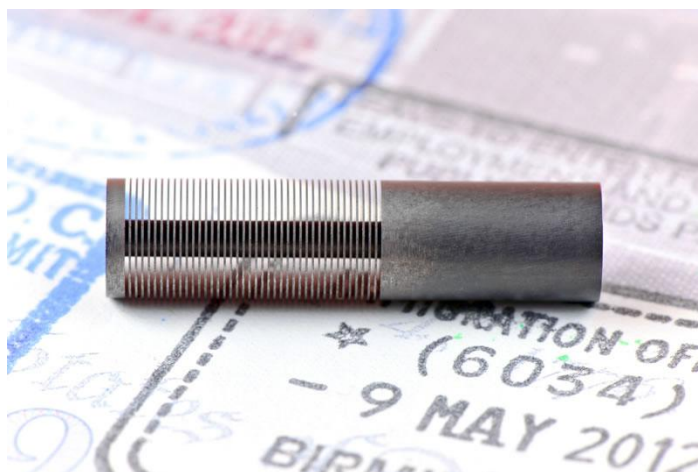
Multi-kanálová měděná elektroda [23].
